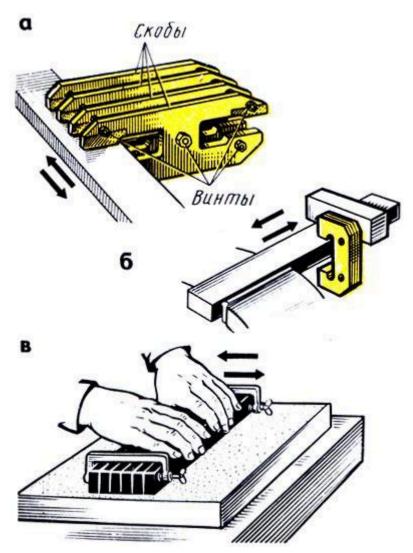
Притирка тонких и узких деталей: а - скоб, скрепленных винтами, б - пакета деталей, скрепленных заклепками, б - скрепленных струбцинами
